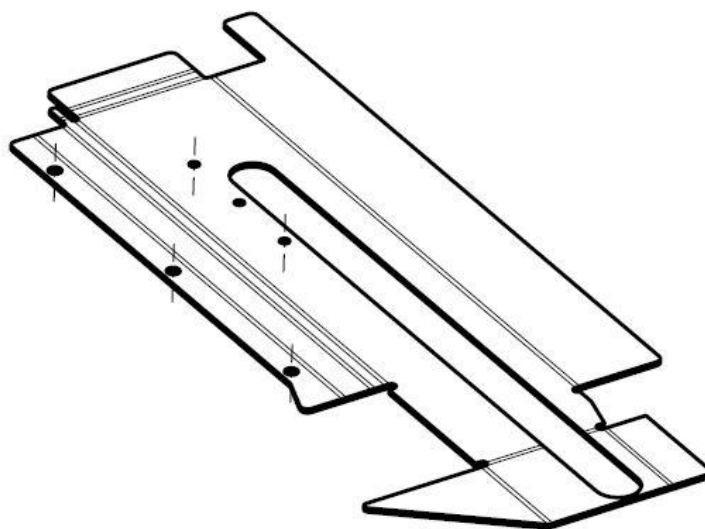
; Bestehendes Seitenteil als ebenes Blech mit Bohrungen und Öffnung für die Gasdruckfeder
